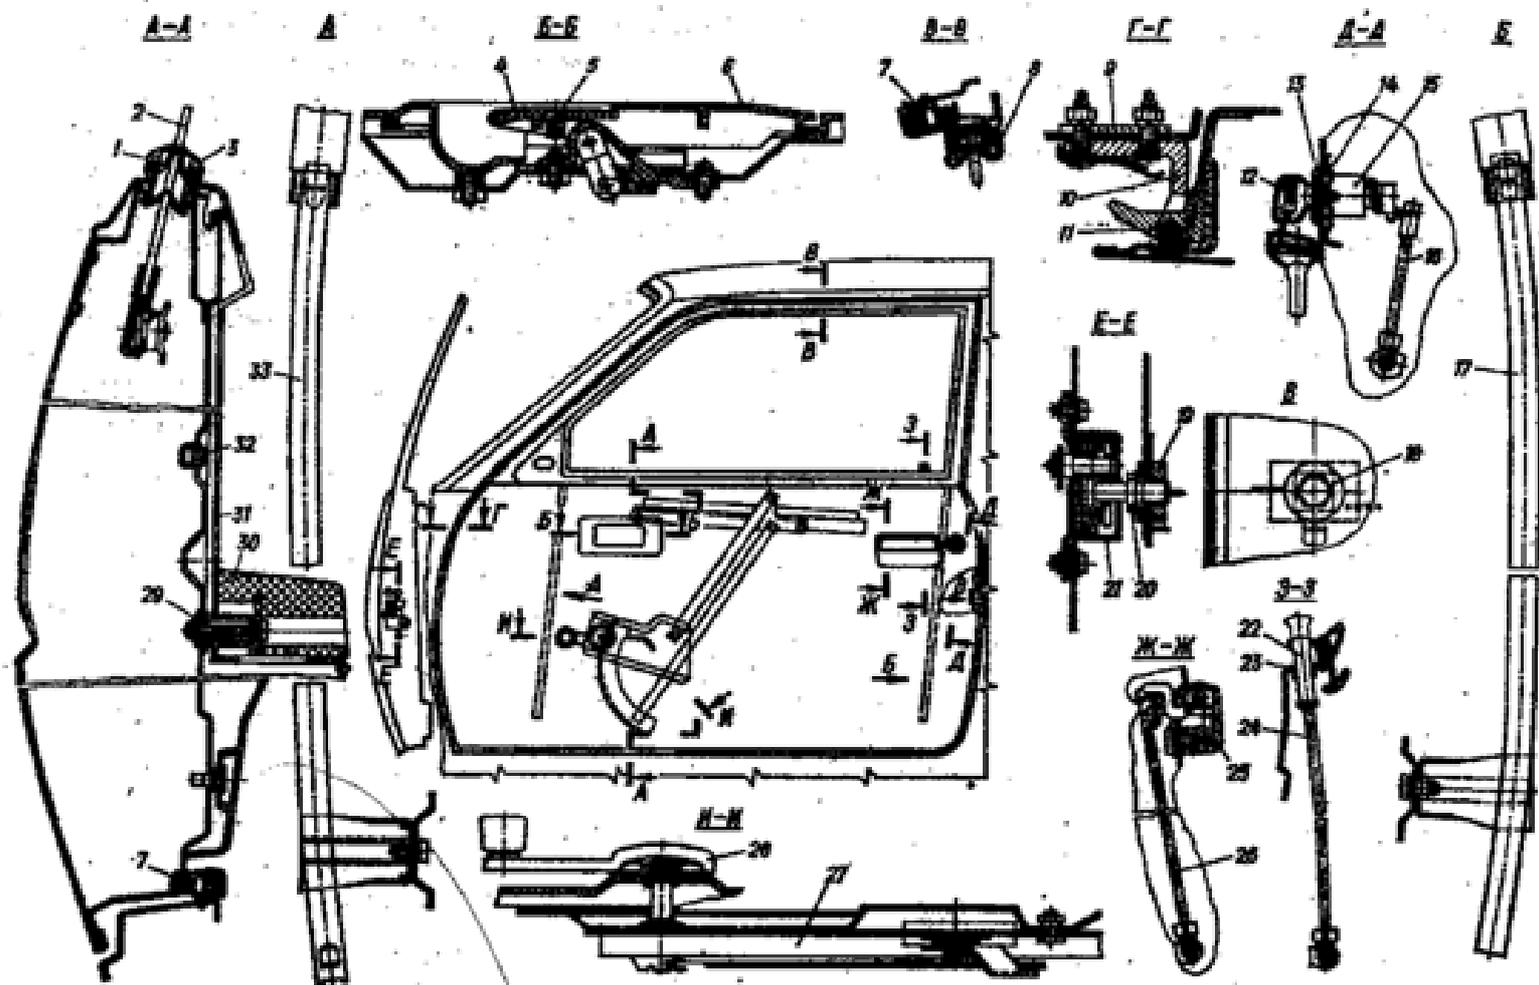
Арматура боковой двери трехдверного автомобиля: 1 - уплотнитель подоконный наружный; 2 - стекло опускаемое в сборе; 3 - уплотнитель подоконный внутренний; 4 - ручка внутренняя; 5 - заглушка к ручке; 6 - облицовка ручки внутренней; 7 - вставка уплотнителя двери; 8 - уплотнитель стекла; 9 - пластина; 10 - петля; 11 - ось петли; 12 - ключи двери; 13 - уплотнитель выключателя; 14 - скоба крепления выключателя; 15 - выключатель замка; 16 - тяга выключателя; 17 - стойка правая; 18 - шайба фиксатора замка; 19 - пластина фиксатора; 20 - фиксатор замка; 21 - замок двери; 22 - кнопка; 23 - розетка; 24 - тяга; 25 - ручка двери; 26 - тяга привода наружной ручки; 27 - стеклоподъемник в сборе; 28 - ручка; 29 - гайка пластинчатая; 30 - подлокотник; 31 - обивка двери; 32 - держатель тяги; 33 - стойка левая.
